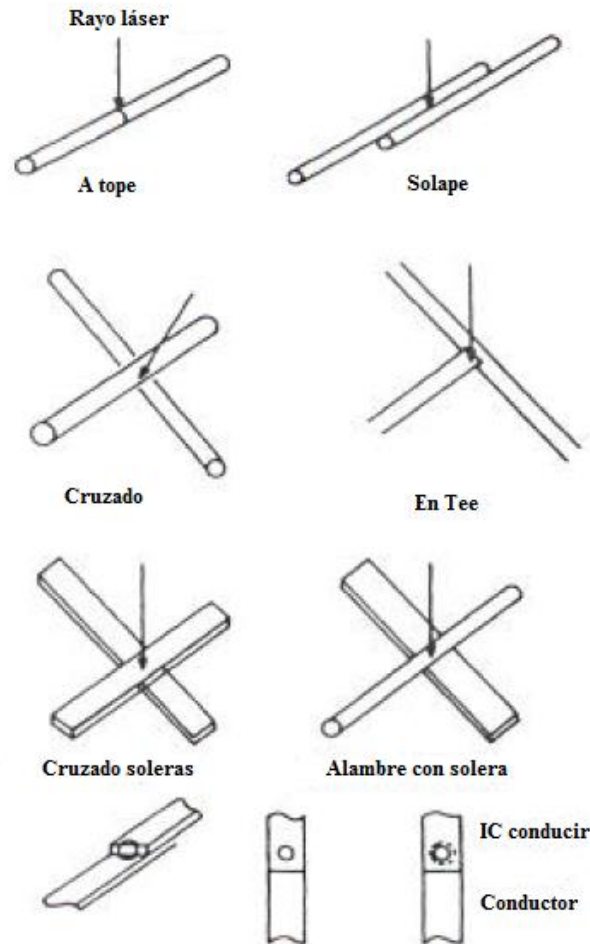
Configuraciones de micro soldaduras láser.
